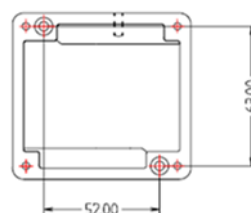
Крепежные отверстия MS2002+ боковой стенки корпуса
